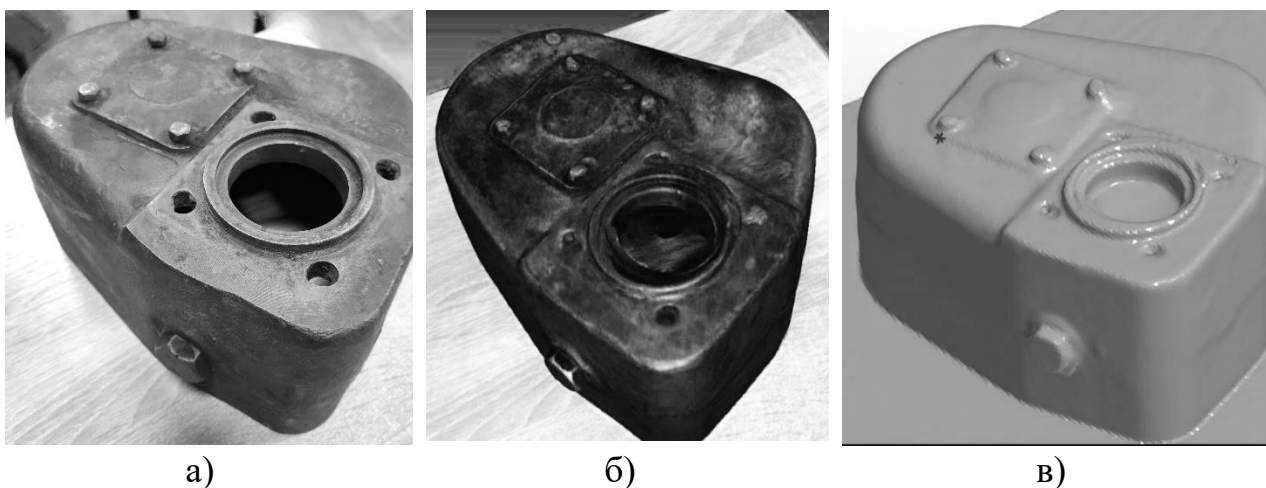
Корпус редуктора (а); результат сканування (б); 3d модель корпусу (в)
